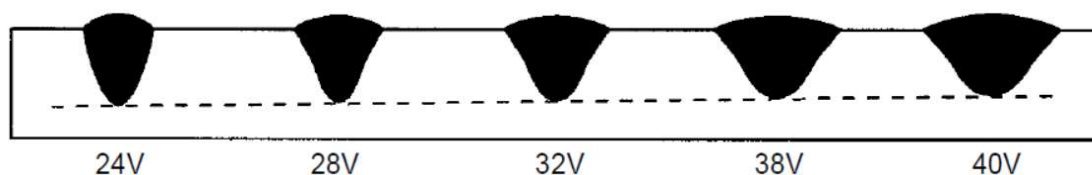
Efecto del voltaje en la geometría del cordón de soldadura (8).
